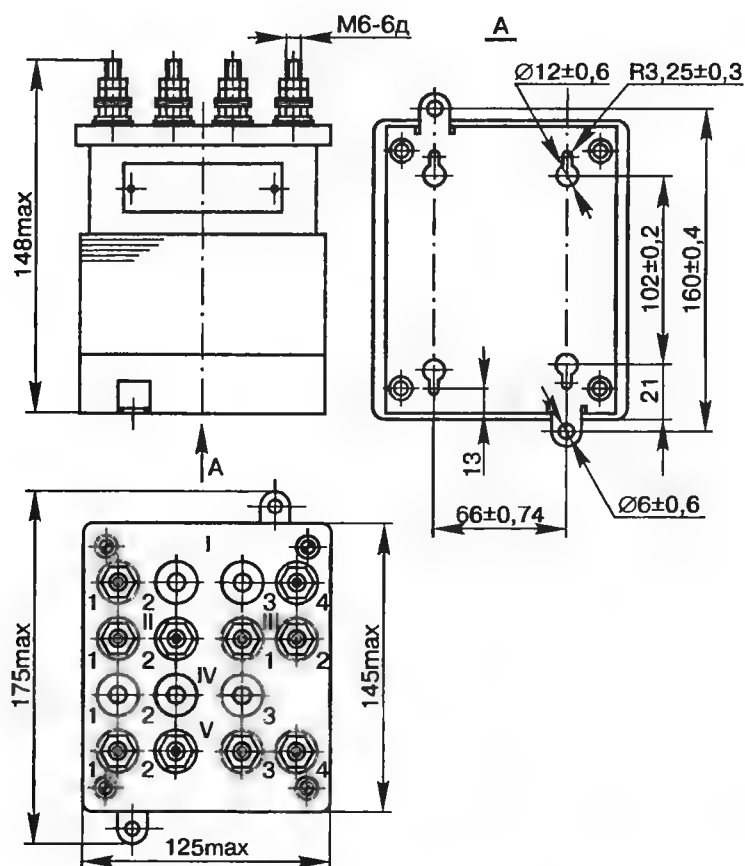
Присоединительные и габаритные размеры трансформатора СОБС-2М
